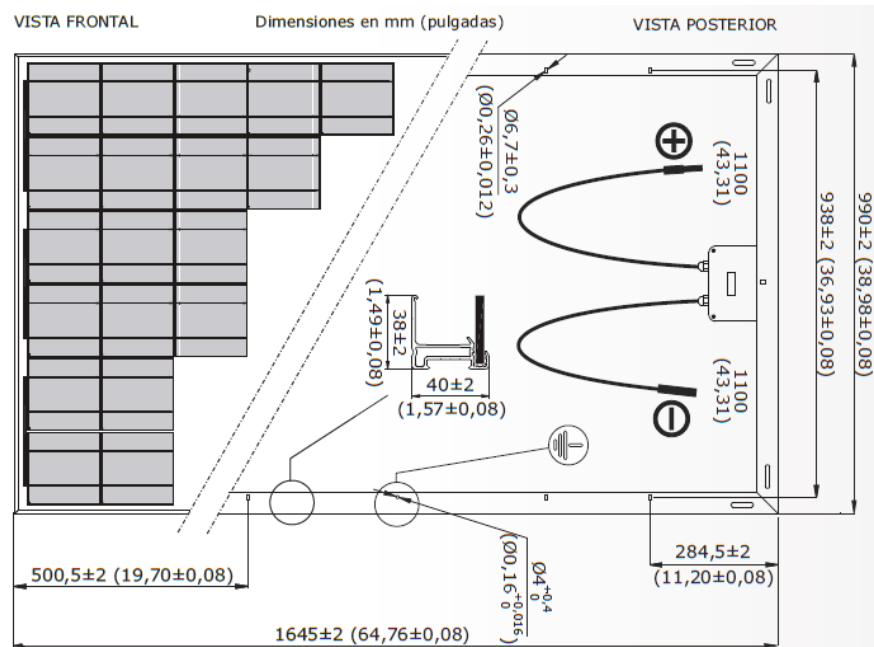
Vista genérica de la construcción del módulo fotovoltaico. Fuente: Ficha técnica módulo FV.
